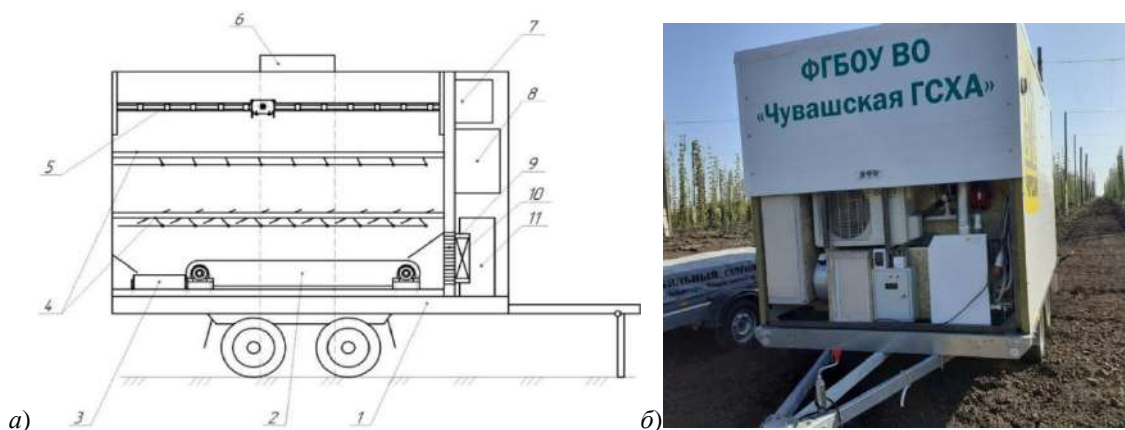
Хмелесушилка (а – схема: 1 – мобильное шасси, 2 – транспортер промежуточный; 3 – транспортер выгрузной; 4 – модуль поворотной-стеллажной; 5 – механизм выравнивающий; 6 – транспортер загрузочный, 7 – испаритель, 8 – конденсатор-компрессор; 9 – радиатор; 10 – вентилятор; 11 – нагреватель; б – общий вид с газгольдером)
